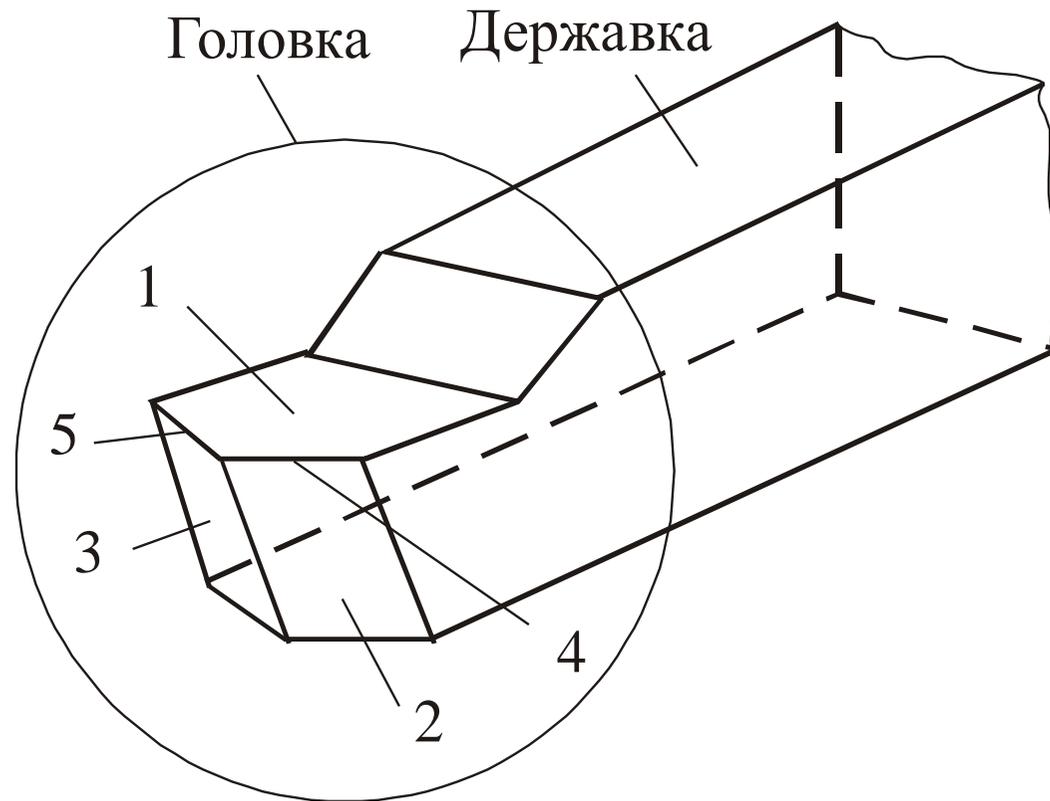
Конструктивные элементы токарного резца: 1 – передняя поверхность; 2 – главная задняя поверхность; 3 – вспомогательная задняя поверхность; 4 – главная режущая кромка; 5 – вспомогательная режущая кромка
